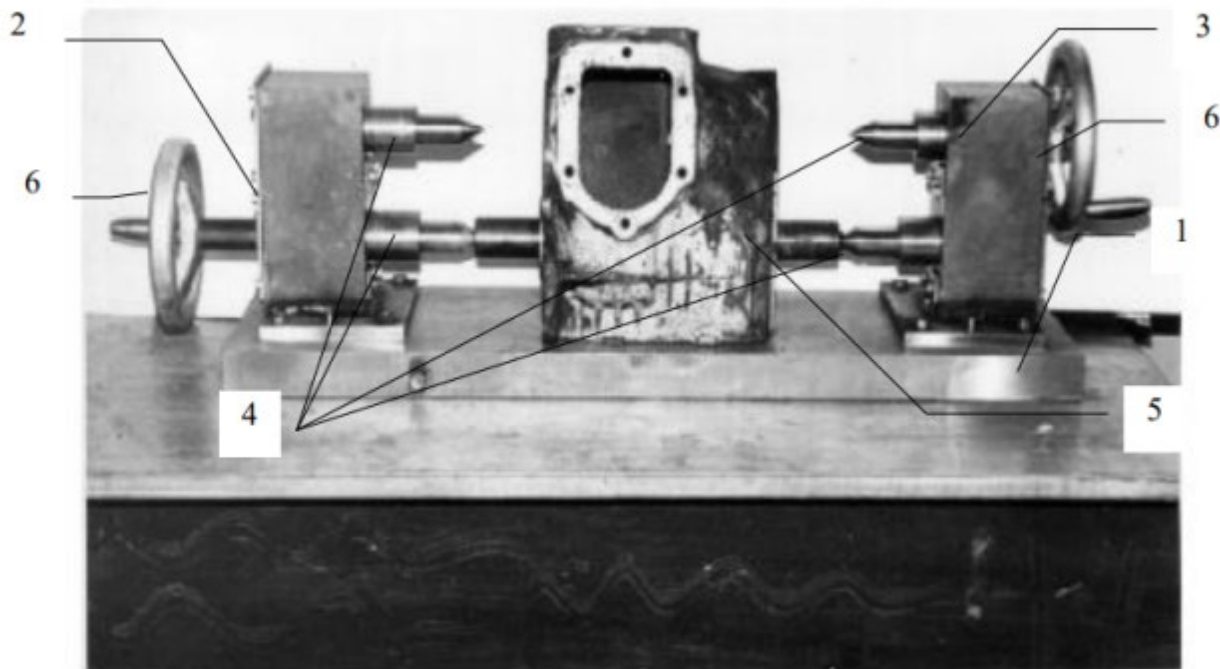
Оснащення для формування підшипникових гнізд з полімерним покриттям у корпусі коробки передач: 1 – плита; 2 – ліва стійка; 3 – права стійка; 4 – центри; 5 – нижня качалка; 6 – маховики
